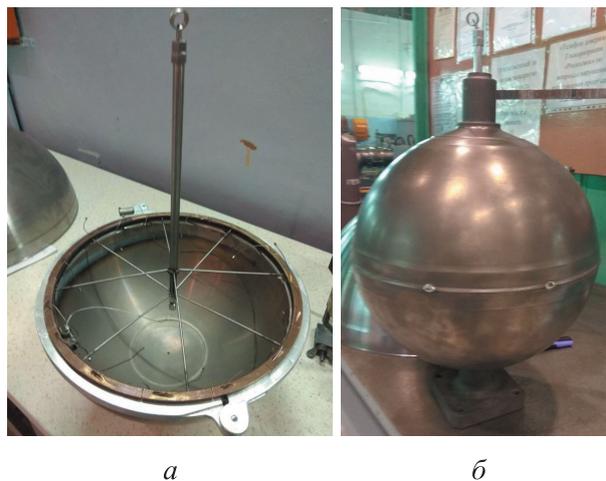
Фрагменты сборки защитного приспособления и баллона:
